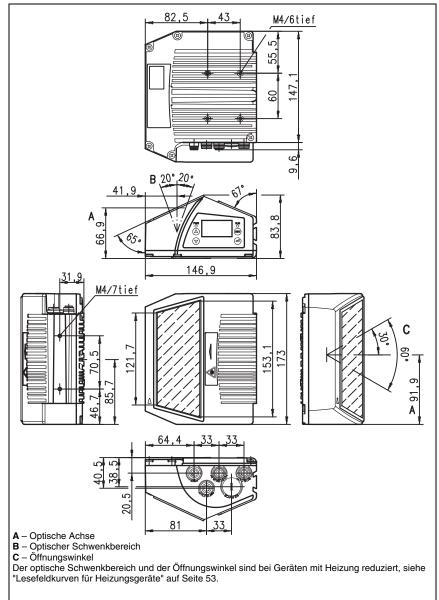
Maßzeichnung Scanner mit Schwenkspiegel BCL 508i O...100
